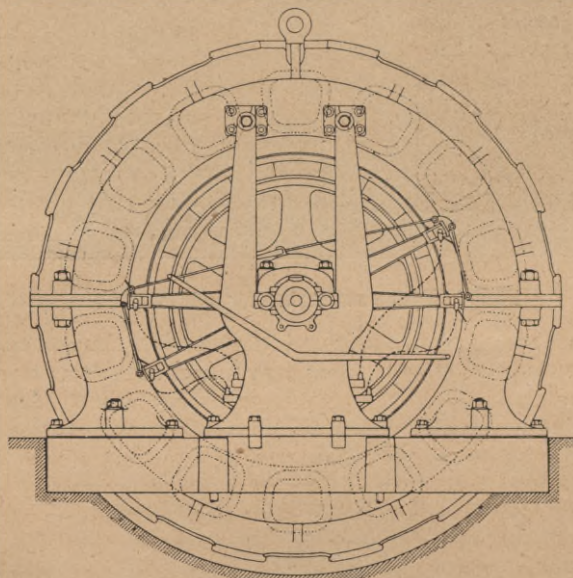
Dynamo-Maschine für 350,000 Voltampère.
